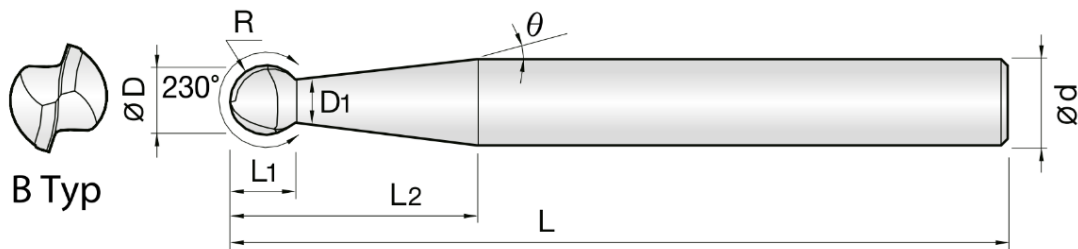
Krátka, guľová fréza do 68 HRC od PM-TECH [33].
